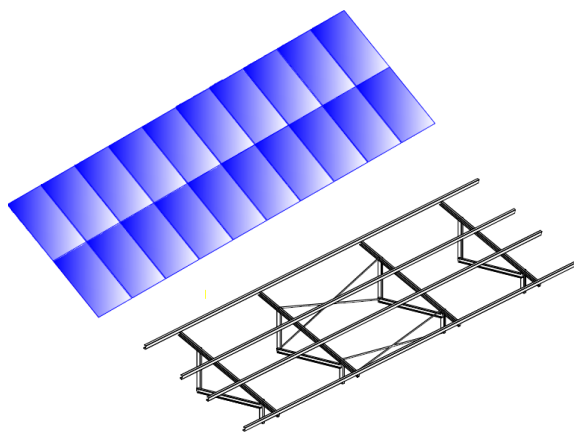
Vista frontal de la estructura. Fuente: Ficha técnica de la estructura, Sunfer
